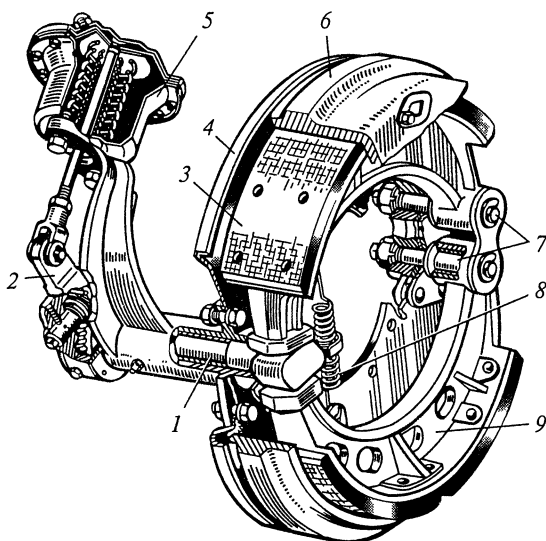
Колесный тормозной механизм грузового автомобиля:
